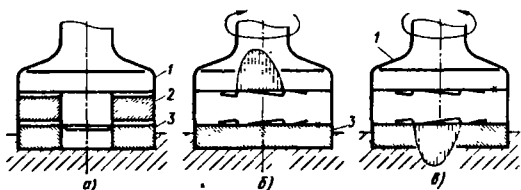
Реверсивный подшипник с промежуточной плавающей шайбой
